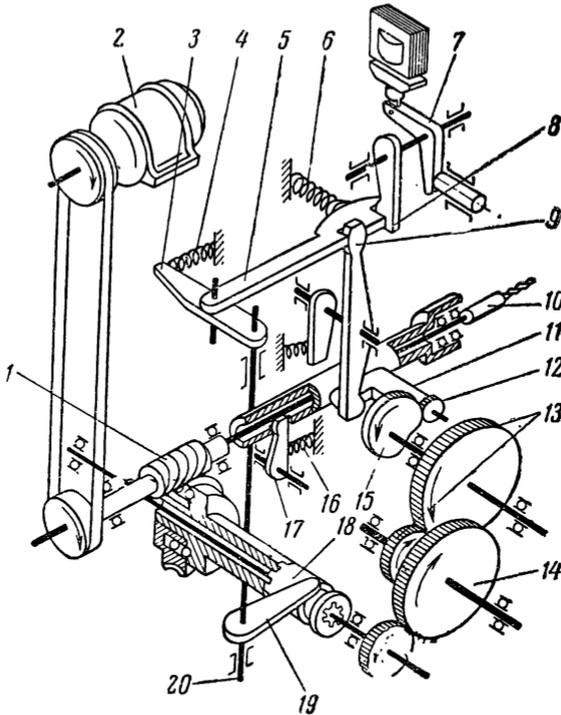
Схема действия силовой головки двухстороннего центрального станка
